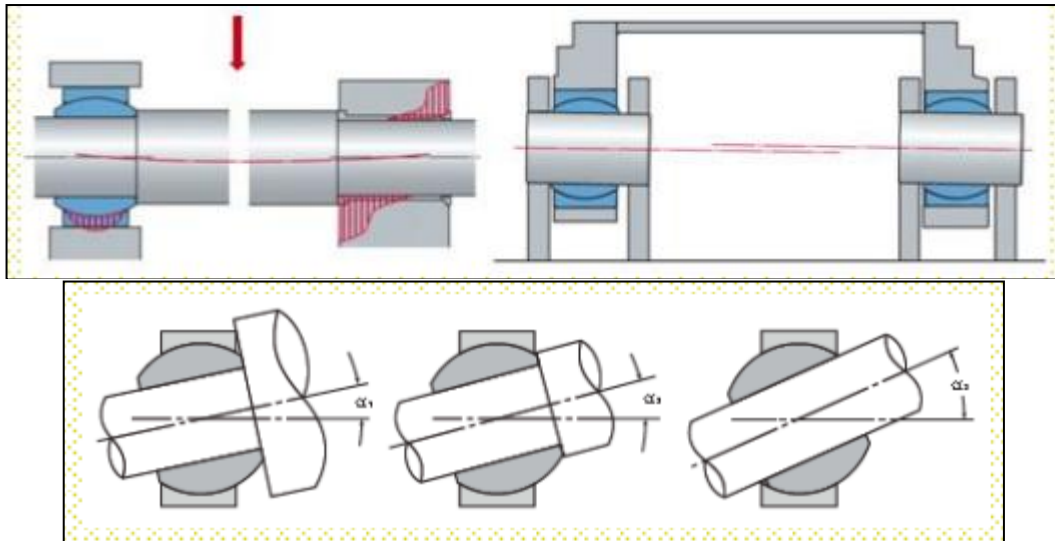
Кут бокового нахилу між кільцями підшипника залежить від форми валу
